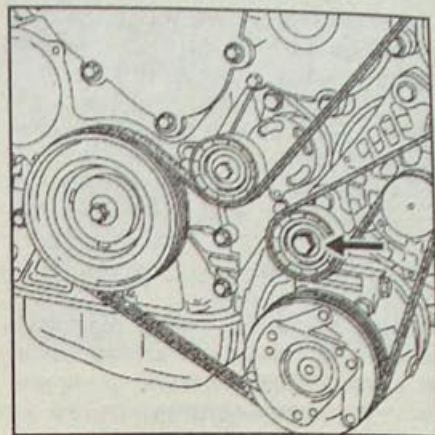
Расположение обводного ролика ремня привода вспомогательного оборудования
